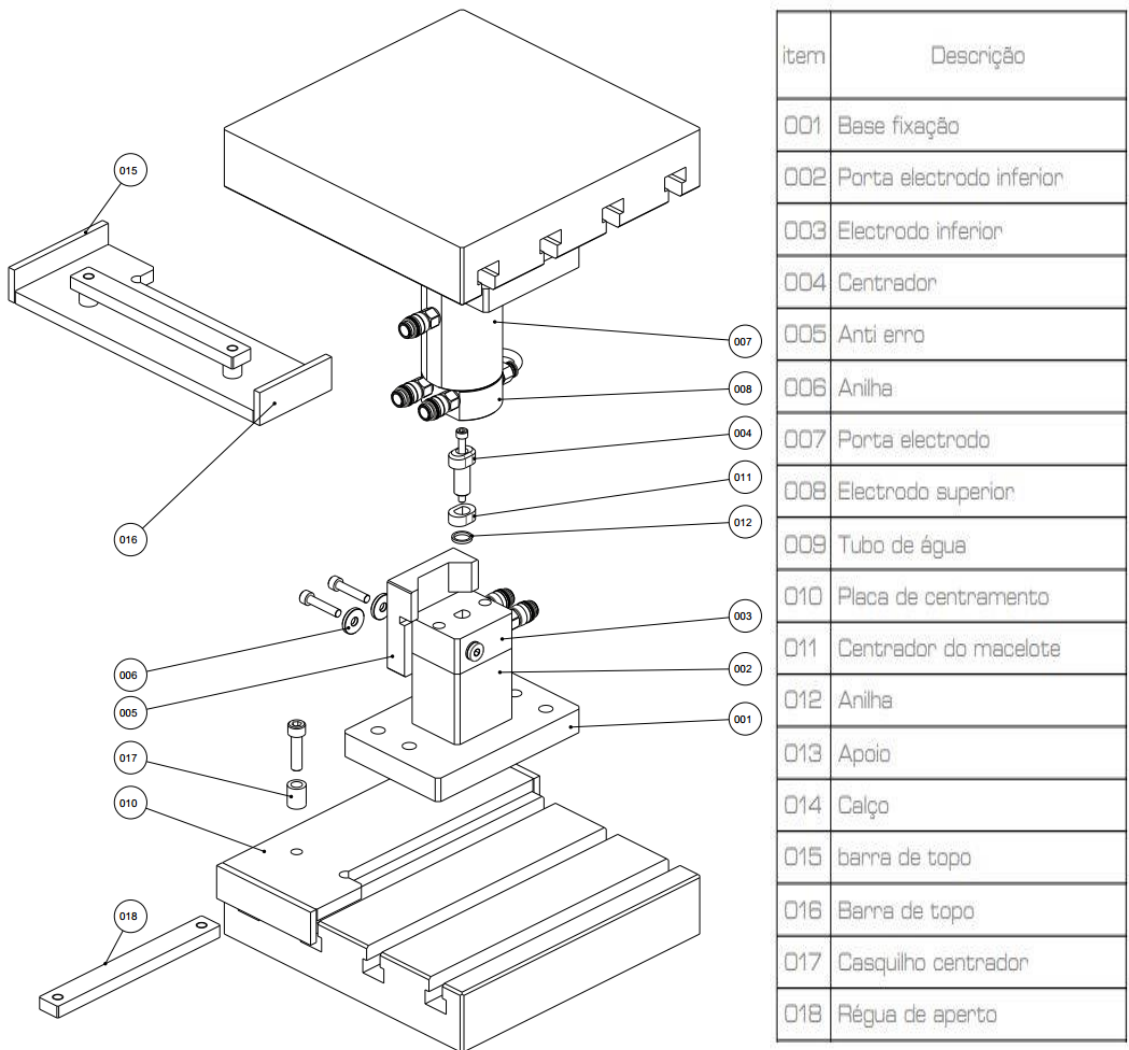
Representação esquemática da ferramenta de soldar os componentes.
